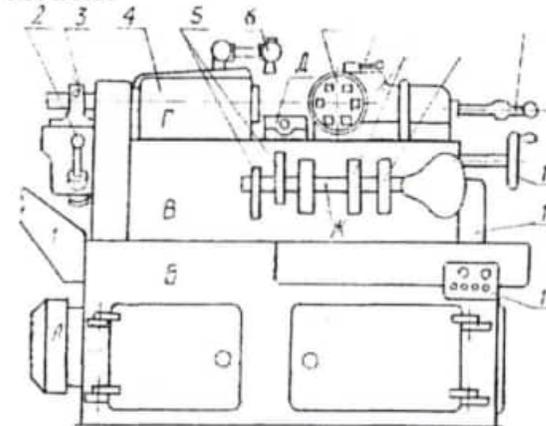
ОБЩИЙ ВИД АВТОМАТА
